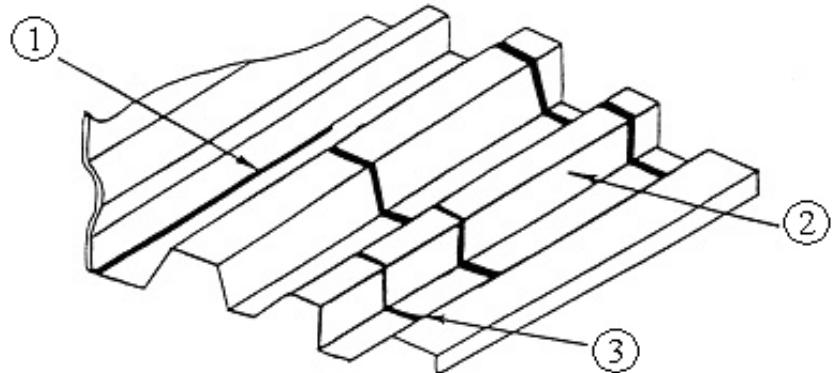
Дефекты металлического пола вагона, ремонтируемые сваркой
